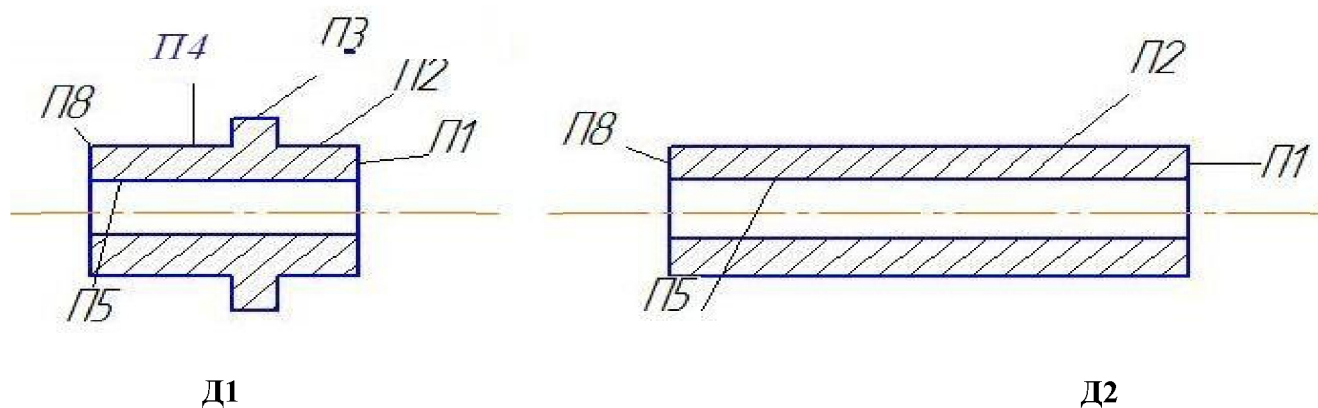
Детали для разработки индивидуальных техпроцессов
